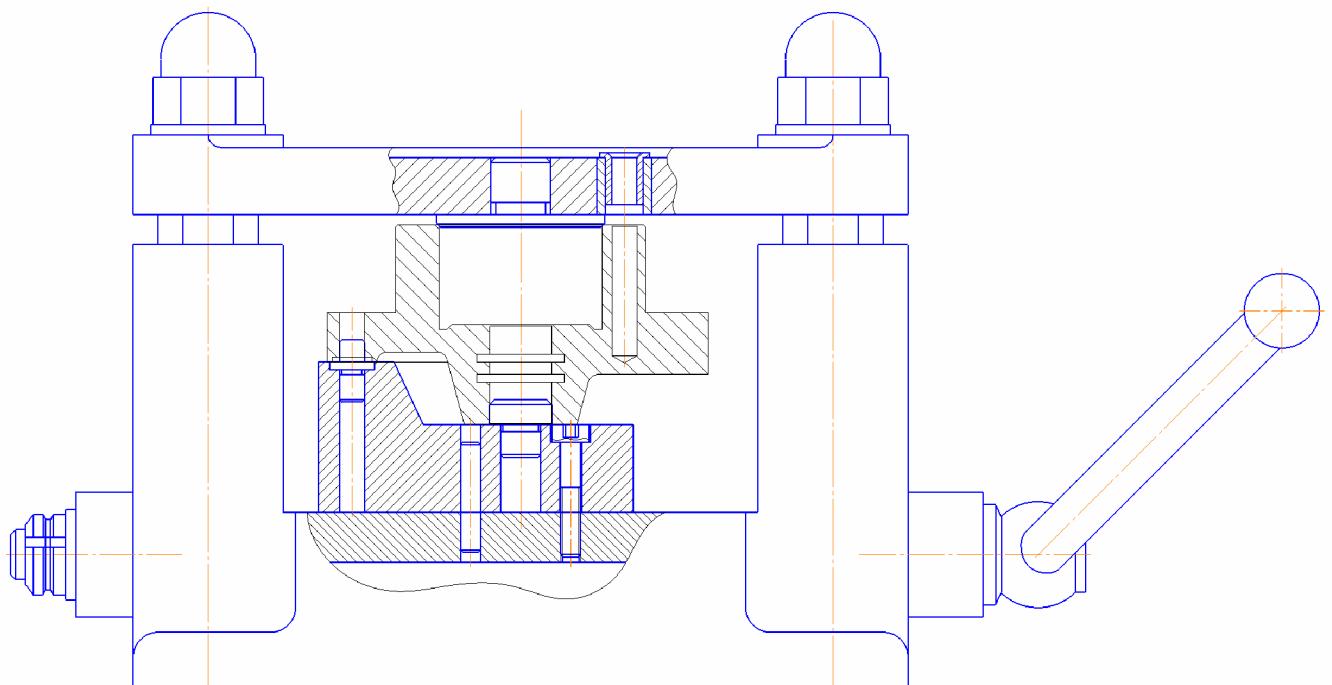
Конструктивна схема верстатного пристосування
